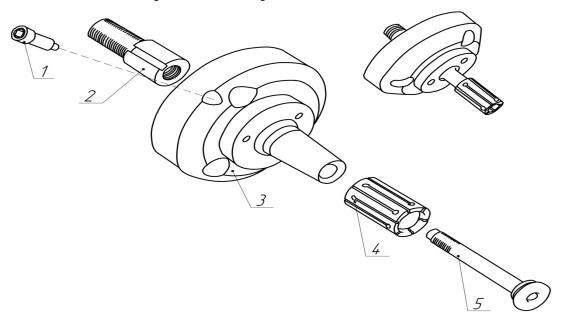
Шпиндельная разжимная фланцевая оправка с механизированным приводом и установкой цанги на конусе оправки: 1, 5 — винты; 2 — резьбовая втулка; 3 — корпус оправки; 4 — цанга
